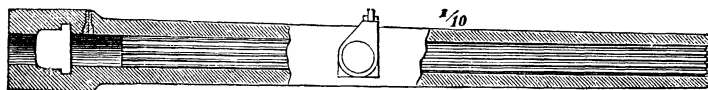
Preussisk 8-ctm.-gjutstålskanon med kilmekanism.
